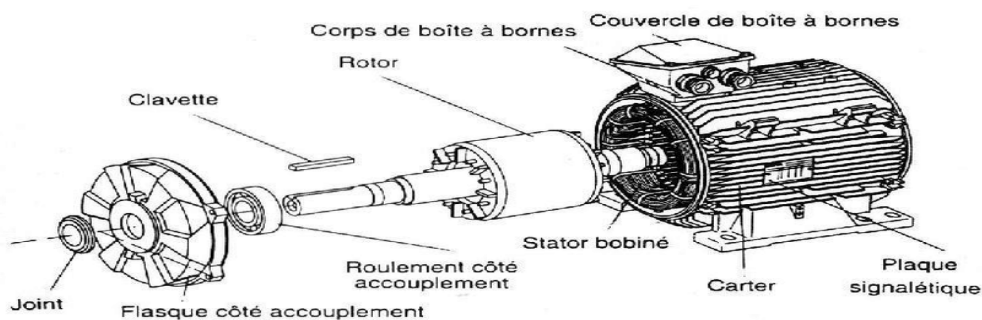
vue éclatée d'une machine asynchrone double étoile
